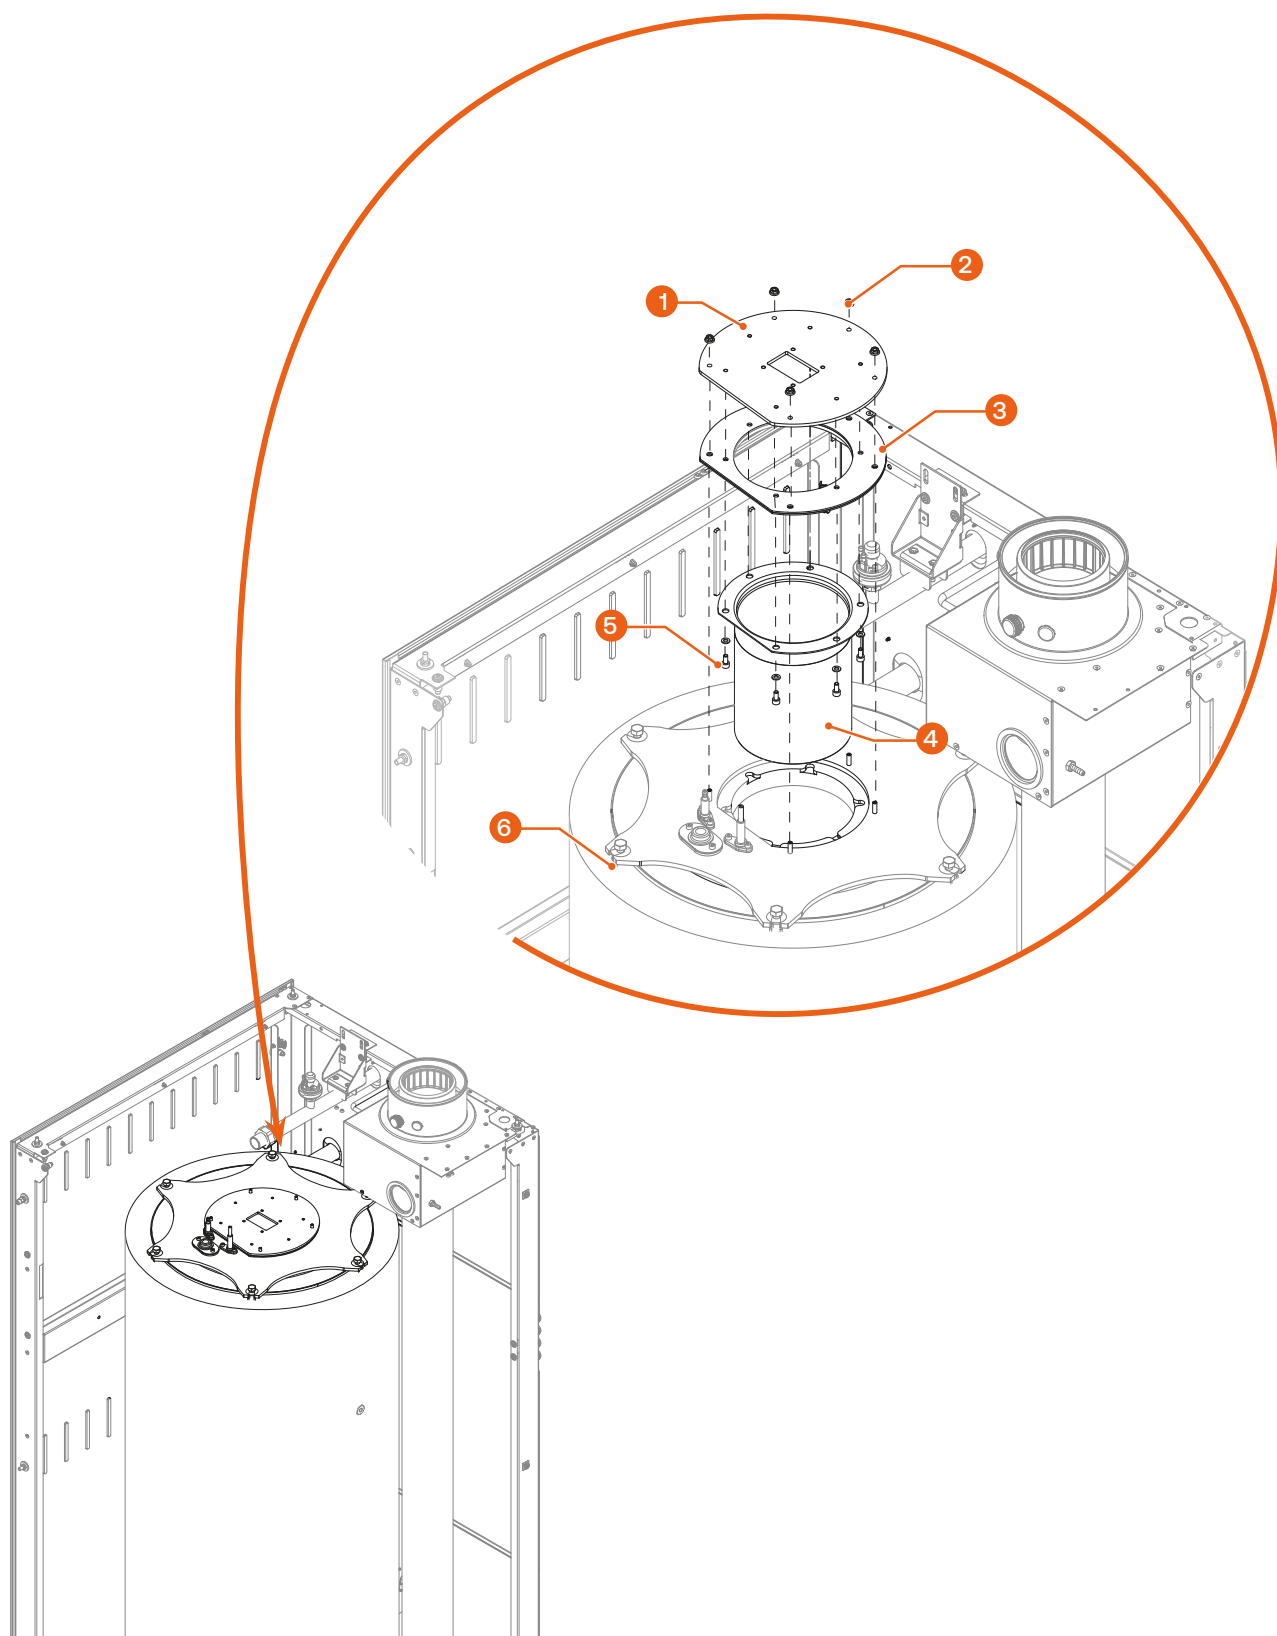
Extracción e instalación del quemador - CoilMaster 100 - 120
